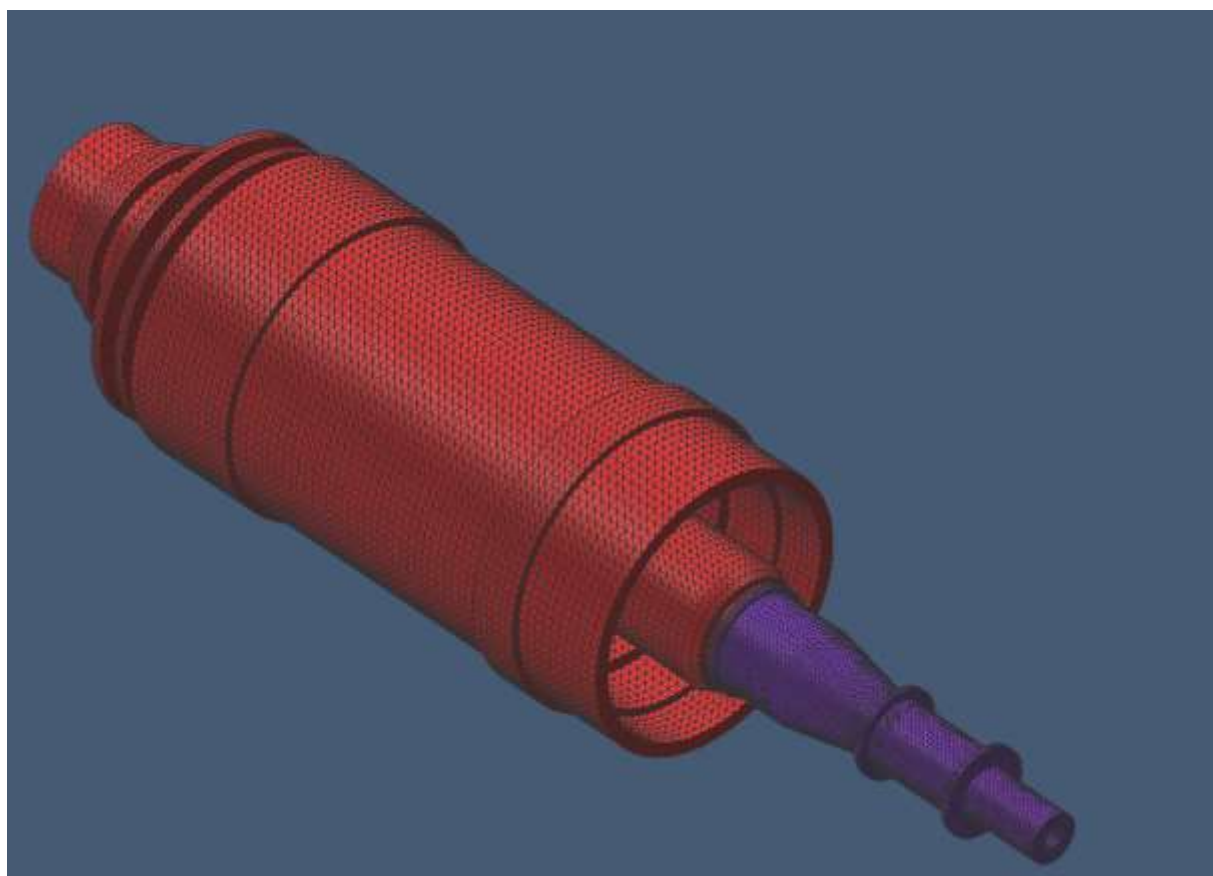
Моделі зварюваних елементів у Simufact Welding
